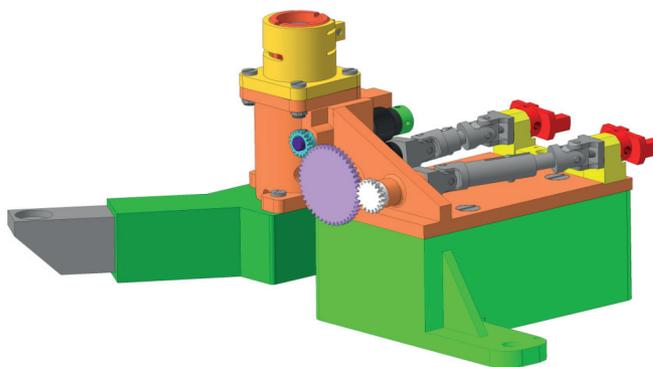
3D двойник под сборки механизма выверки визира мехатронного прибора
